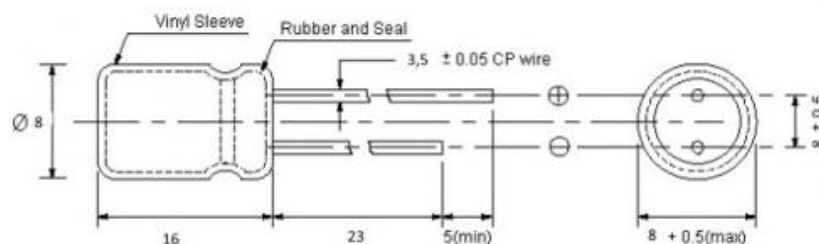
Габаритні розміри конденсатора типу b41828 "Ercos"
